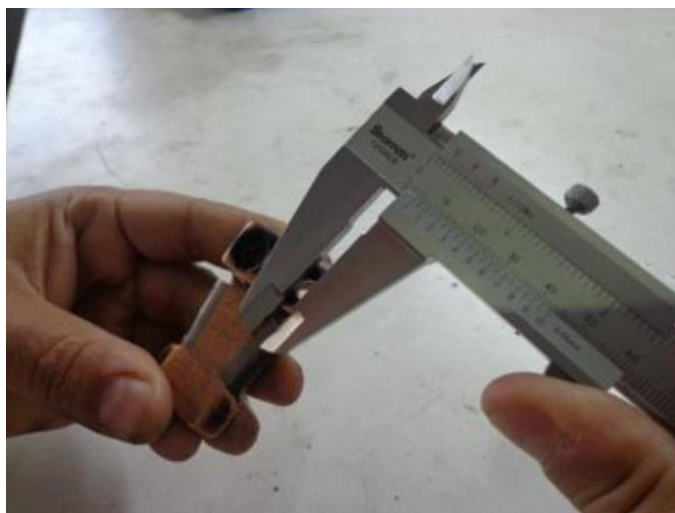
Medição das dimensões de um contato fixo de CDC [31].
